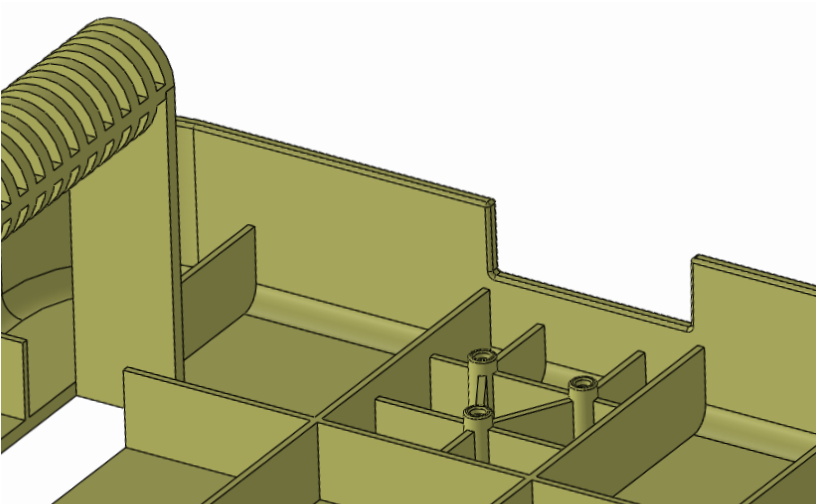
Vista de las torretas y el recorte en el respaldo
